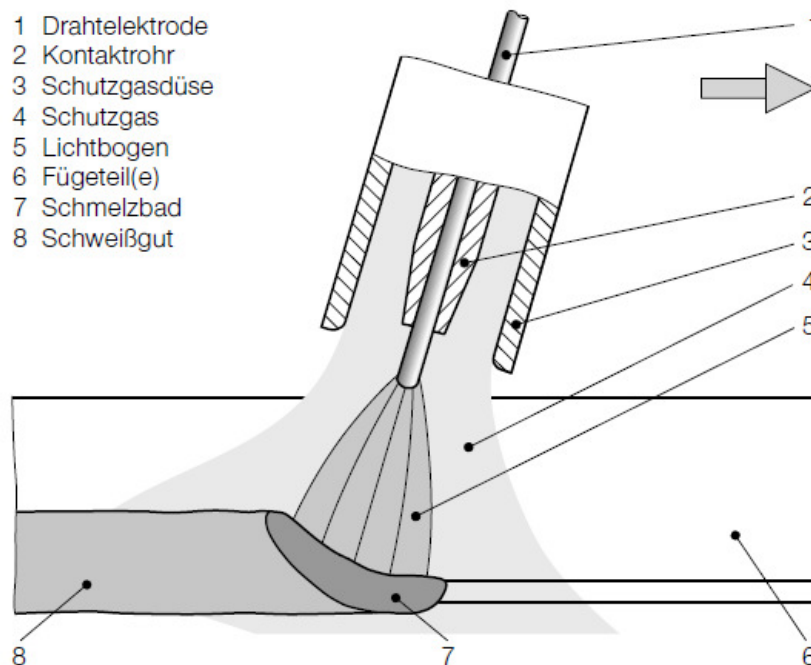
Verfahrensprinzip MIG-Schweißen [9]
